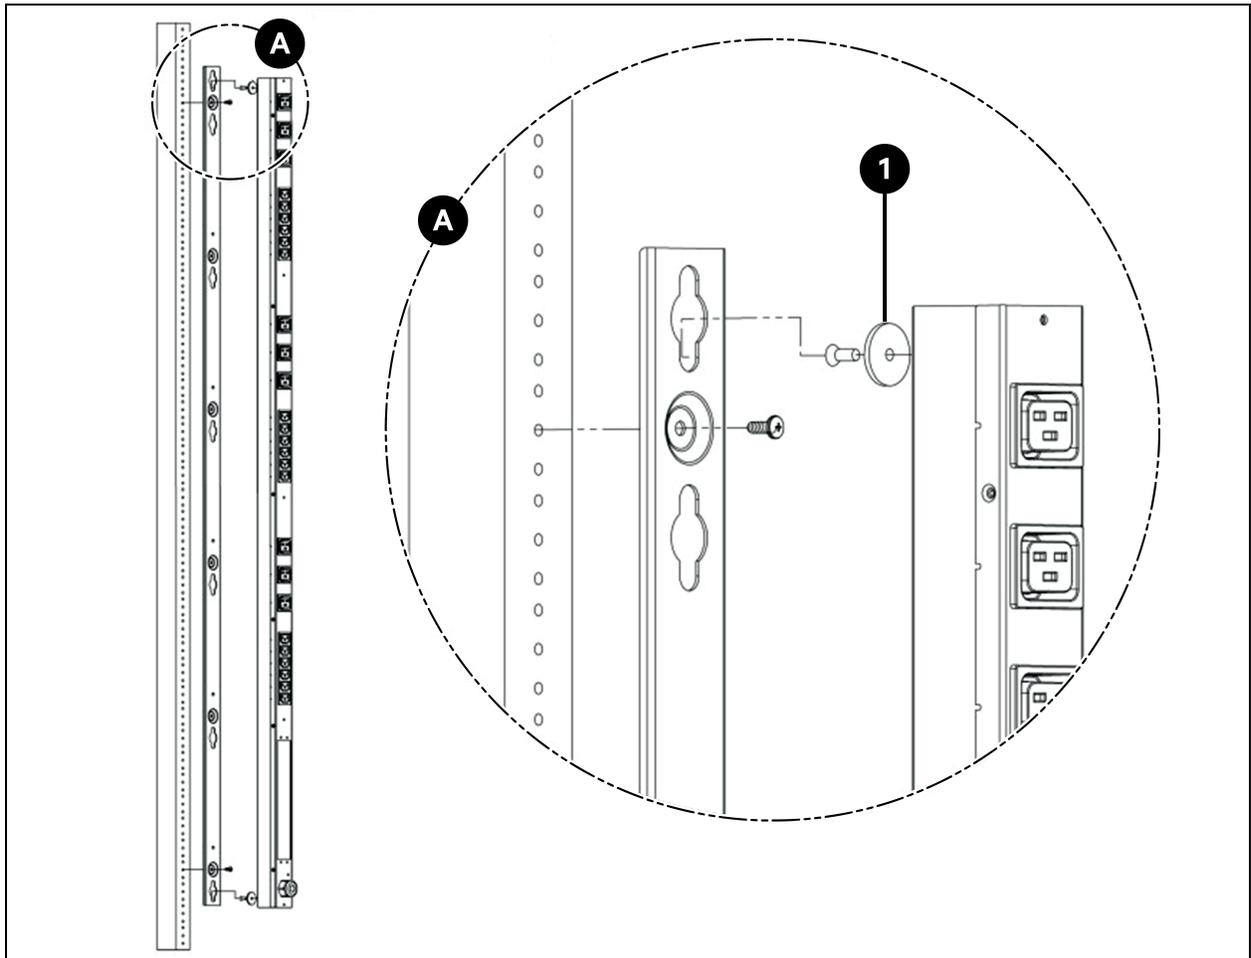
Werkzeuglose Halterungen in voller Länge
